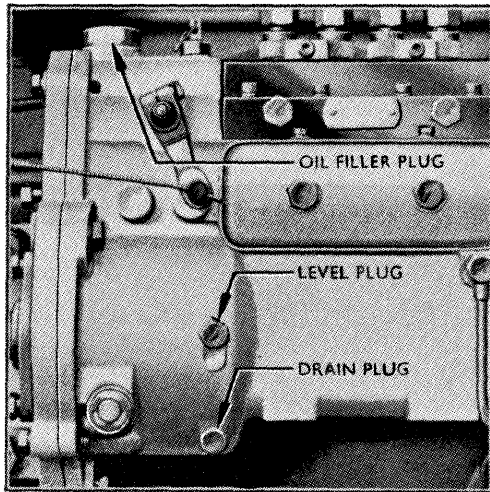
MINIMEC-pumpens oliepåfyldnings-, oliestands- og olieaftapningsskruer. Pumpen smøres med motorolie.
